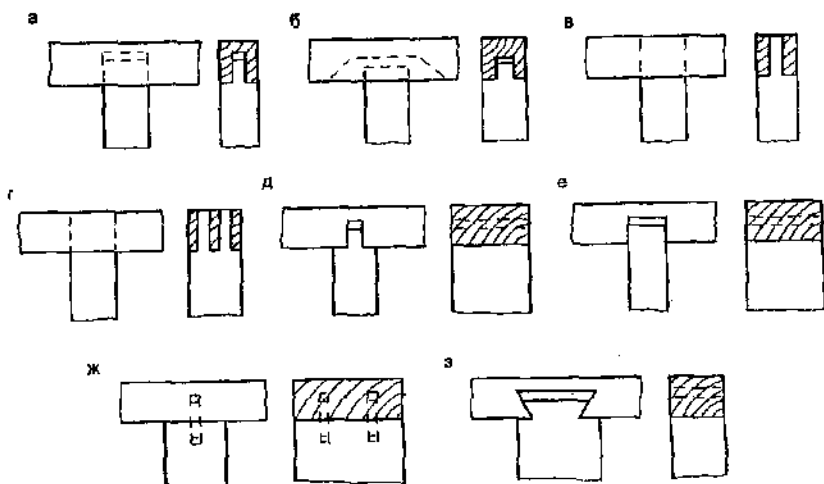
Угловые серединные соединения: а — на шип одинарный несквозной; б — на шип одинарный несквозной в паз; в — на шип одинарный сквозной; г — на шип двойной сквозной; д — а паз и гребень несквозной; е — в паз несквозной; ж — на шипы круглые вставные несквозные; з — на шип «ласточка хвост» сквозной
